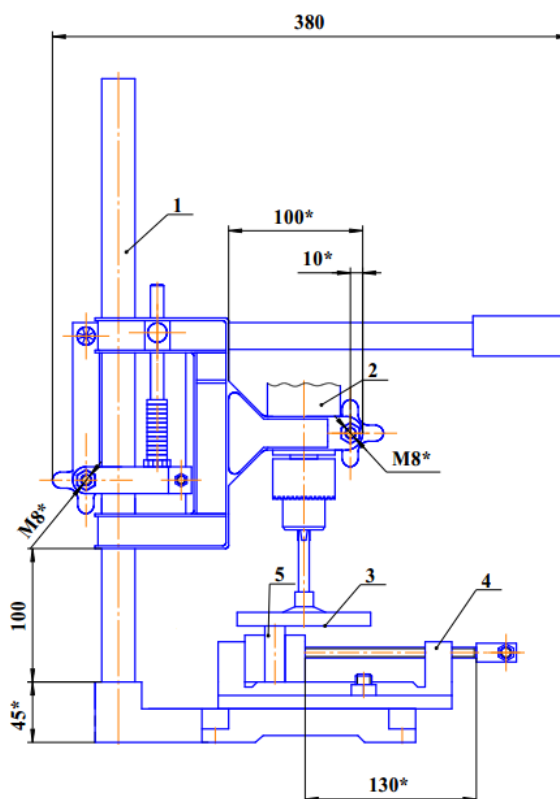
Установка для испытания износостойкости наплавленных образцов [91]
